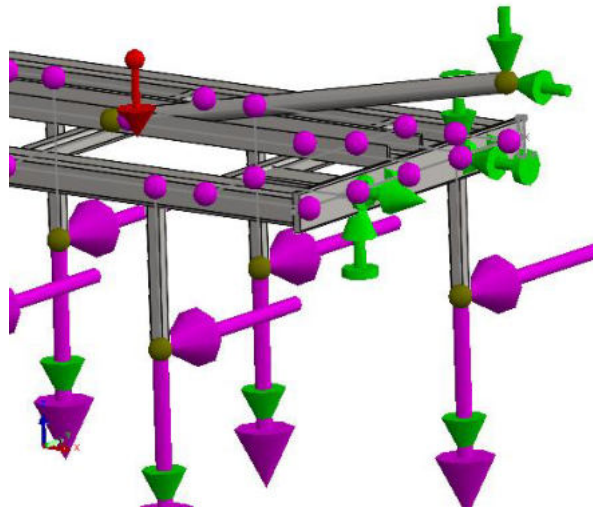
Estructura con condiciones de apoyo para determinar la fuerza del cilindro.
